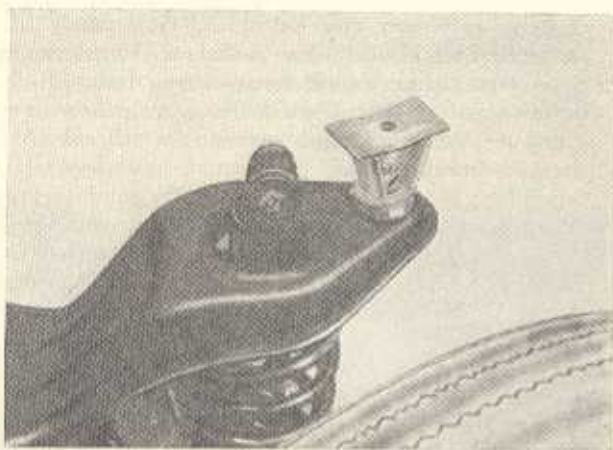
Hintere Karosseriebefestigung, Baumuster 312
